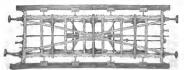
, Pianta d'un treno di vettura di 2.º classe.
